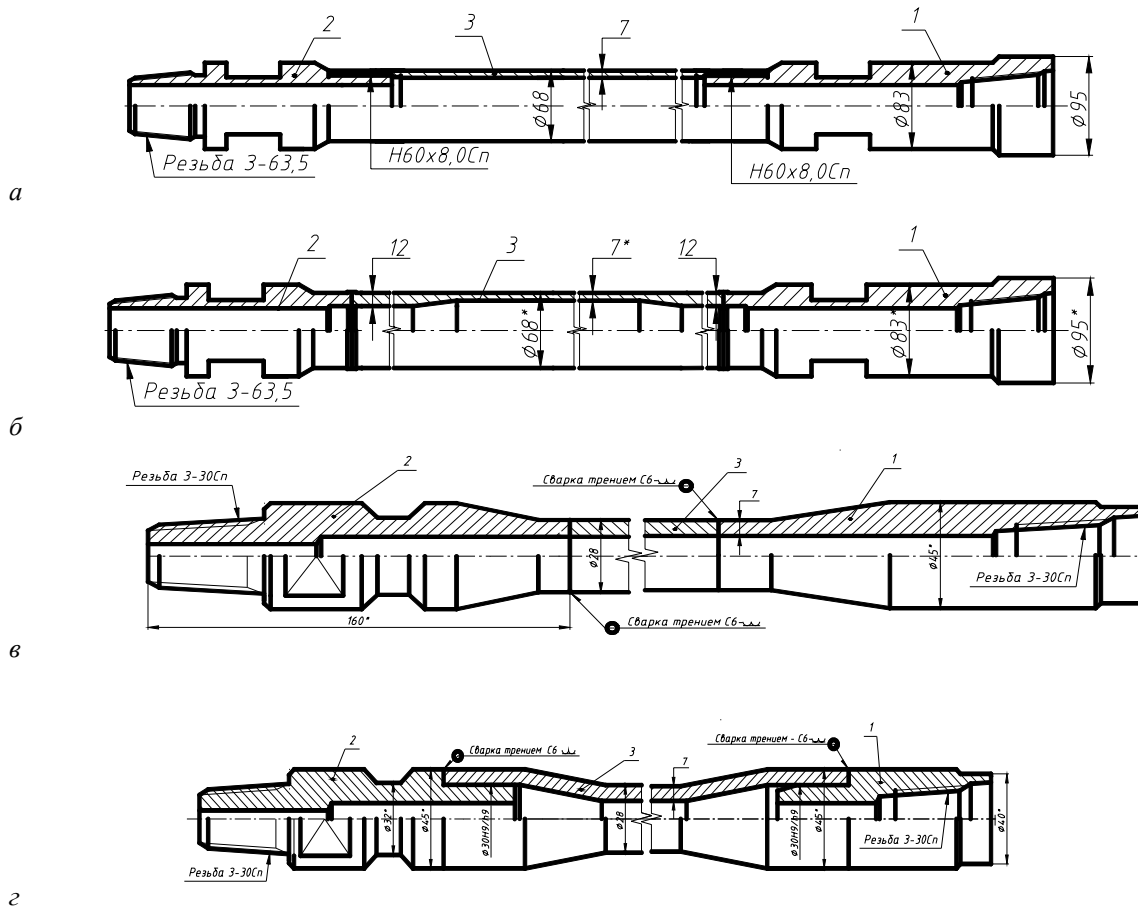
Образцы труб с резьбовыми и приварными элементами замка при нагревании за счет трения: а – буровая труба замкового соединения с ниппельными резьбами присоединения элементов замка 3-63,5; б – буровая труба замкового соединения с приварными замками 3-63,5; в – буровая труба замкового соединения с высаженными концами труб, замковая резьба 3-30Сп; г – буровая труба замкового соединения с приварными замками и раструбными концами гильз, замковая резьба 3-30Сп; 1 – муфта; 2 – ниппель замка; 3 – гильза; 7 – толщина стенки гильзы; 12 – толщина замка гильзы в месте сварного шва
